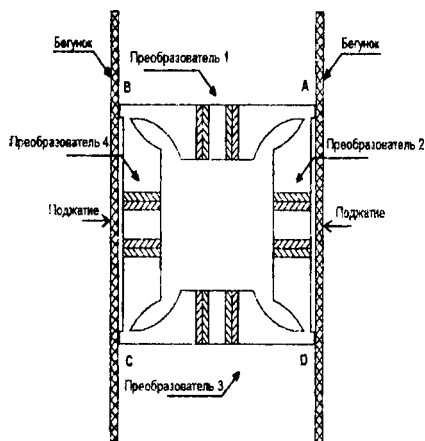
Общий вид статора пьезодвигателя специального вида
